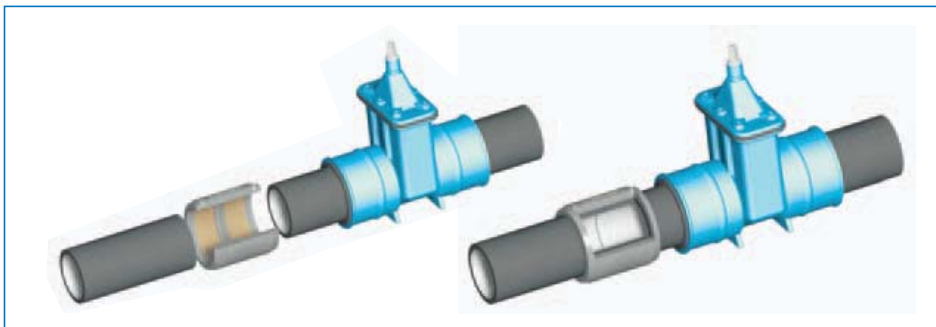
Prinzip des Heizwendelschweißens
